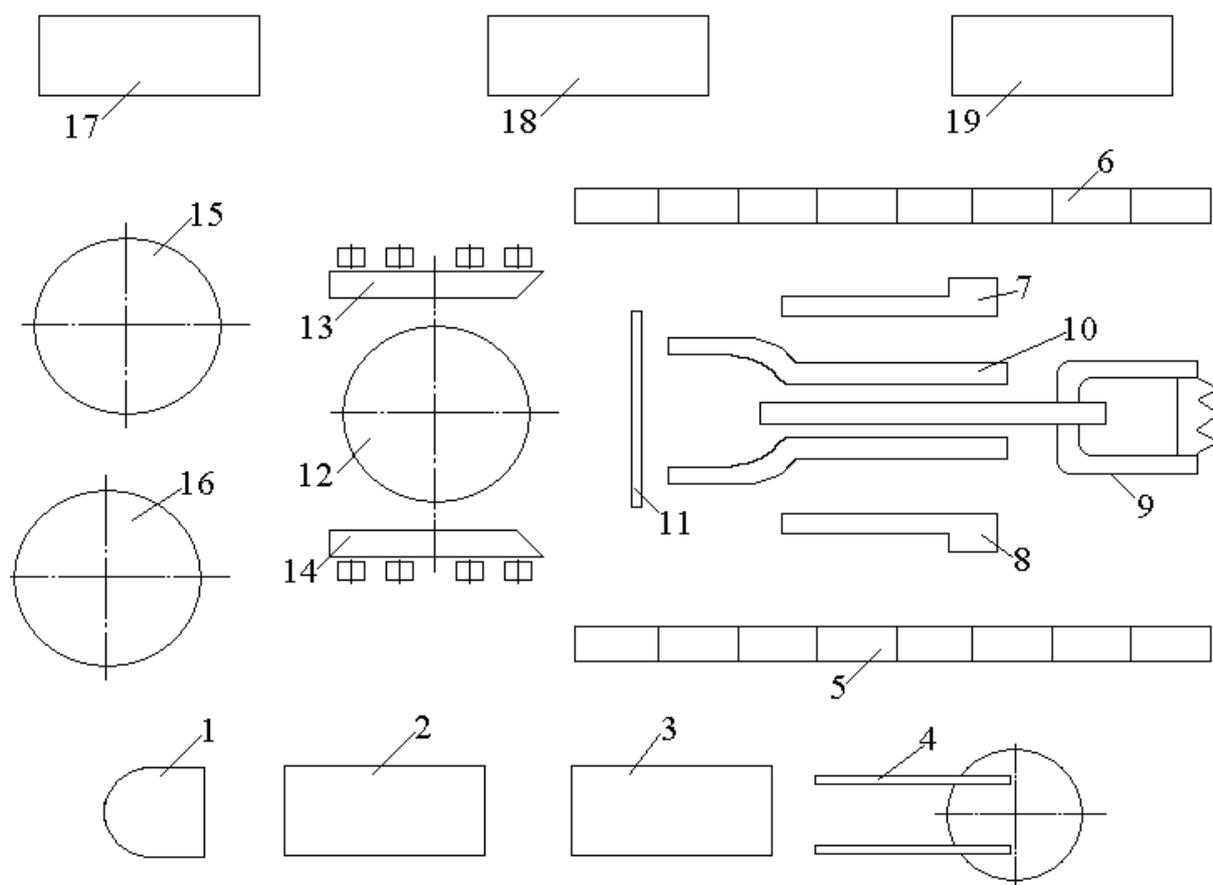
Рациональная схема расположения узлов и механизмов экскаваторов-мехлопат на монтажной площадке: 1 – корпус противовеса; 2 – поворотная платформа; 3 – детали и узлы кузова; 4 – двуногая стойка; 5, 6 – гусеничные цепи; 7, 8 – площадка платформы; 9 – рукоять с ковшом; 10 – стрела; 11 – натяжная ось; 12 – нижняя рама; 13, 14 – гусеничная рама; 15, 16 – верхний и нижний поворотные круги; 17 – электрооборудование; 18 – пневматическое и гидравлическое оборудование; 19 – канатно-полиспастные приспособления
